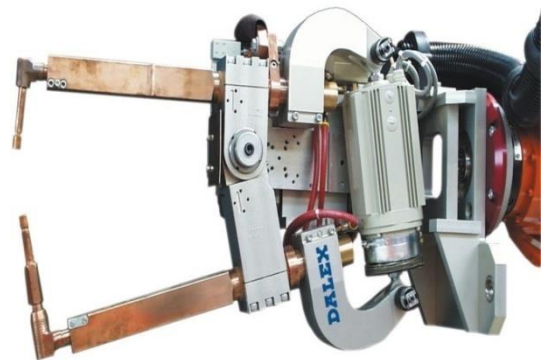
Pince (mécanisme) de soudage par point
